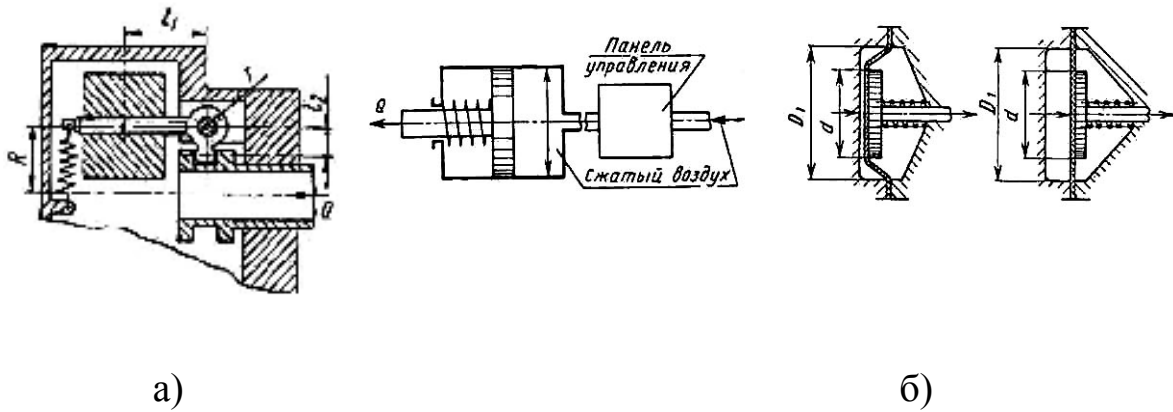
Приводи: а) – механічний; б) – пневматичний.
